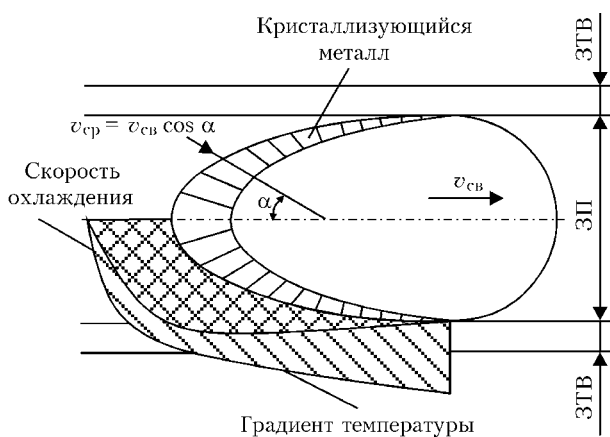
Схема движущейся сварочной ванны и кристаллизации металла
